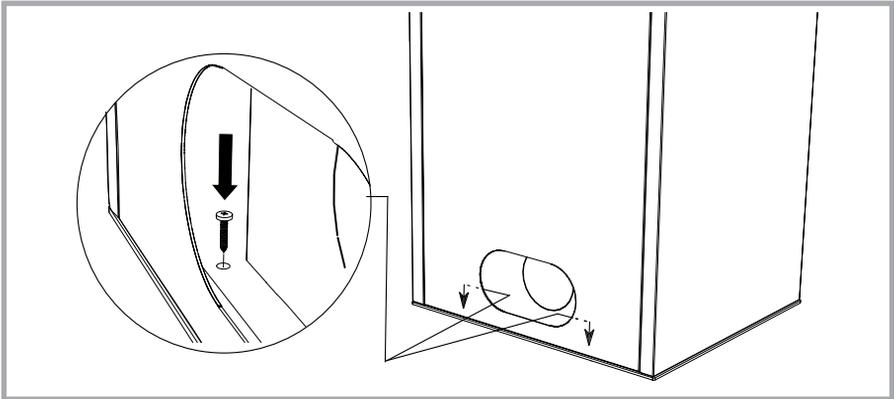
Fixierung des Kaminofens mittels Schrauben.
